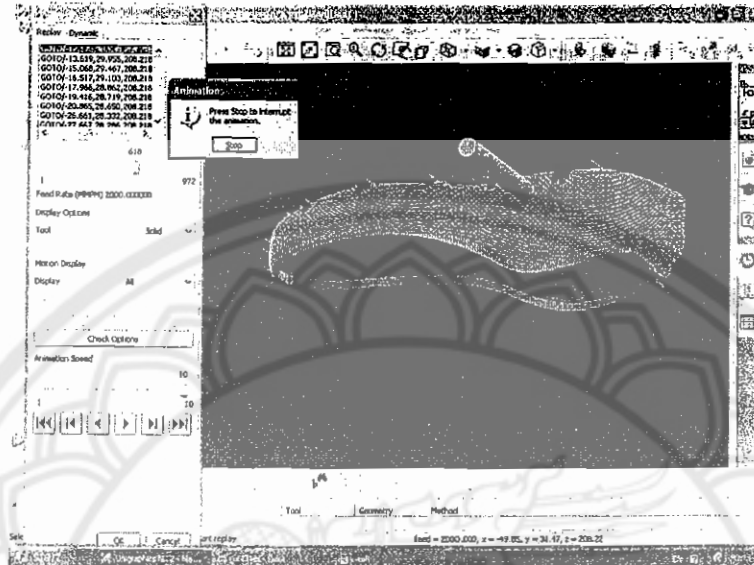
แผนภาพแสดง Tool path: ข้างขวา (END MILL D10)
